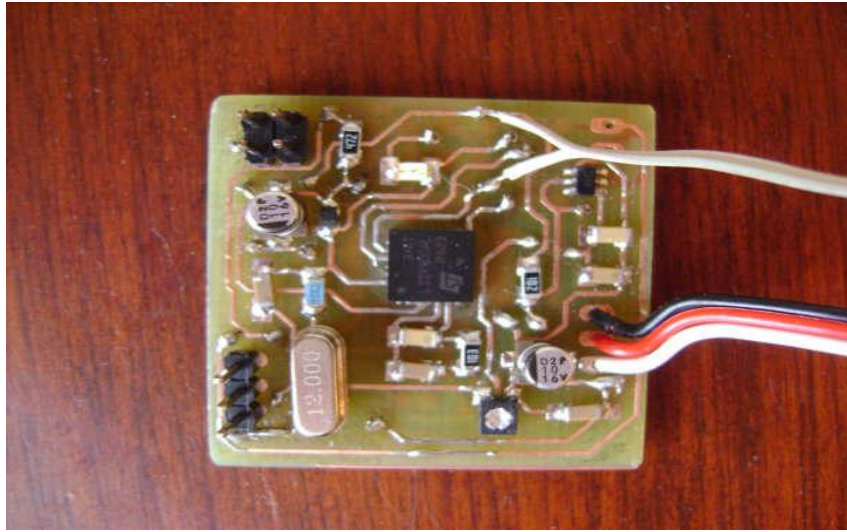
Detalle del dispositivo final, construcción del hardware
